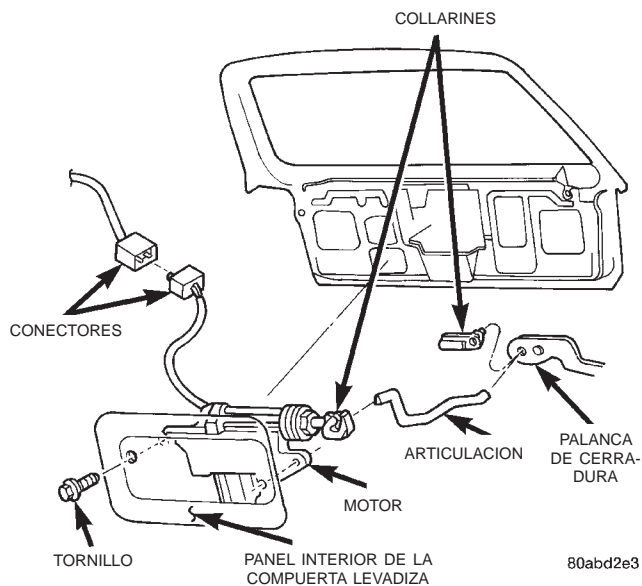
Desmontaje/instalación del motor de cerradura automática de la compuerta levadiza
